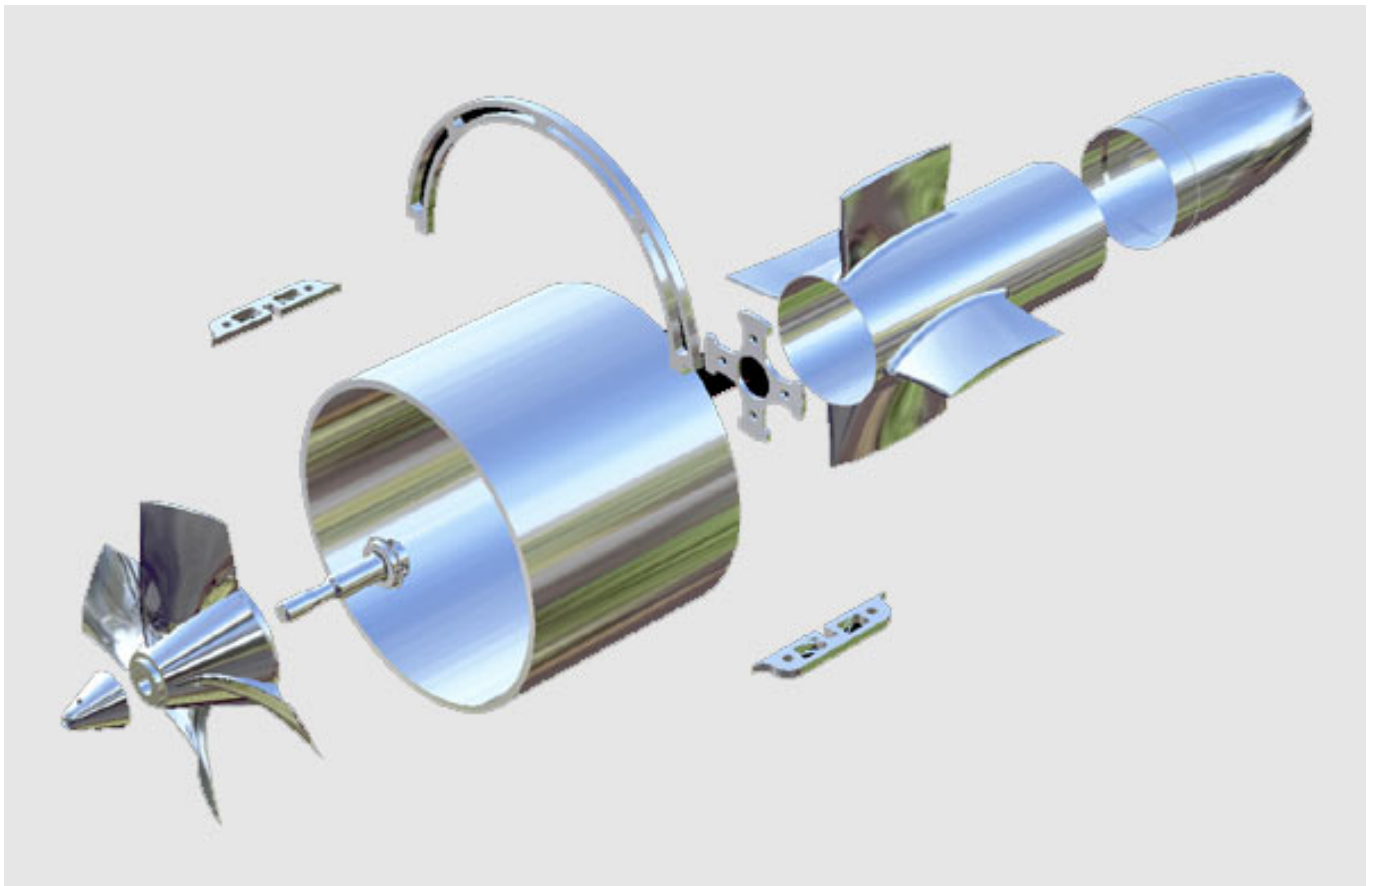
Explosionszeichnung eines DS-51-DIA HDT
